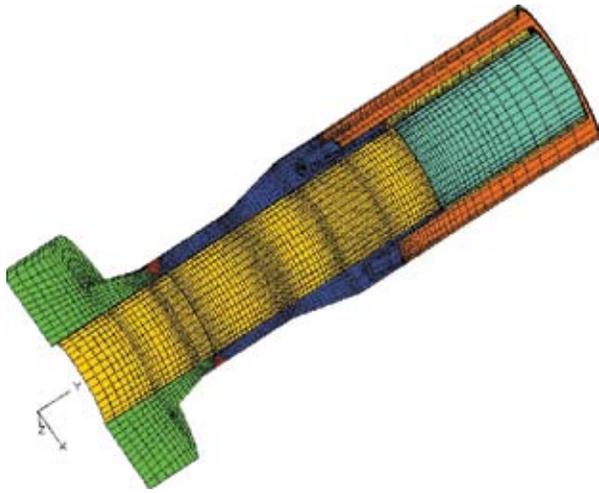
Комплексное объемное моделирование узлов прохода через стенки
